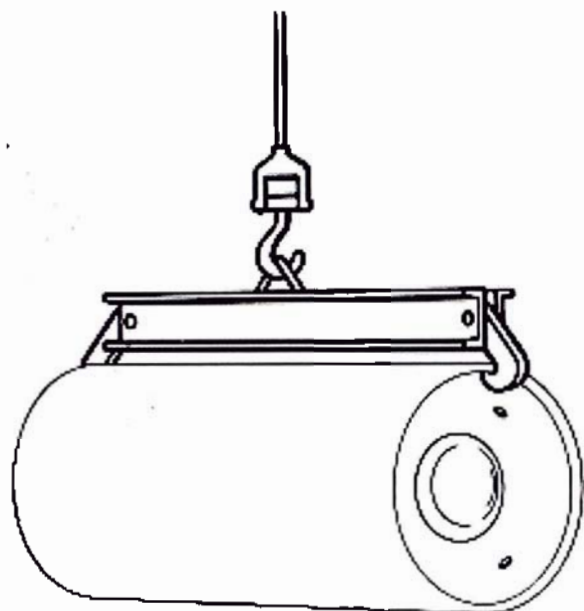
Exemplo de Barra Elevatória para Movimentação de Cilindros Grandes
